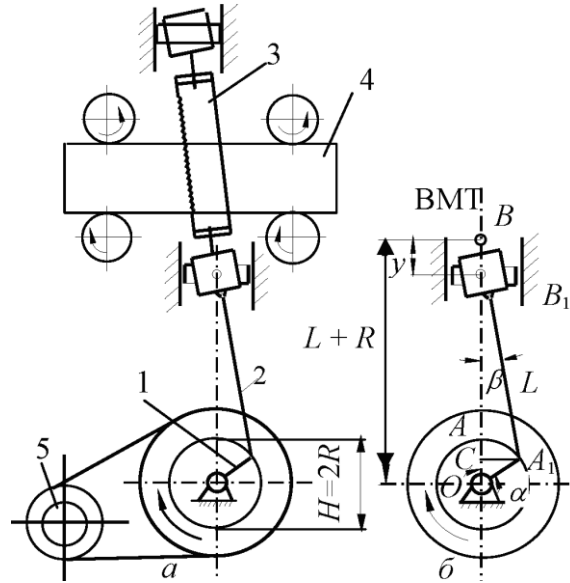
Лісопильна рама: а - схема механізму головного руху; б - кривошипно-шатунно-повзунний механізм
